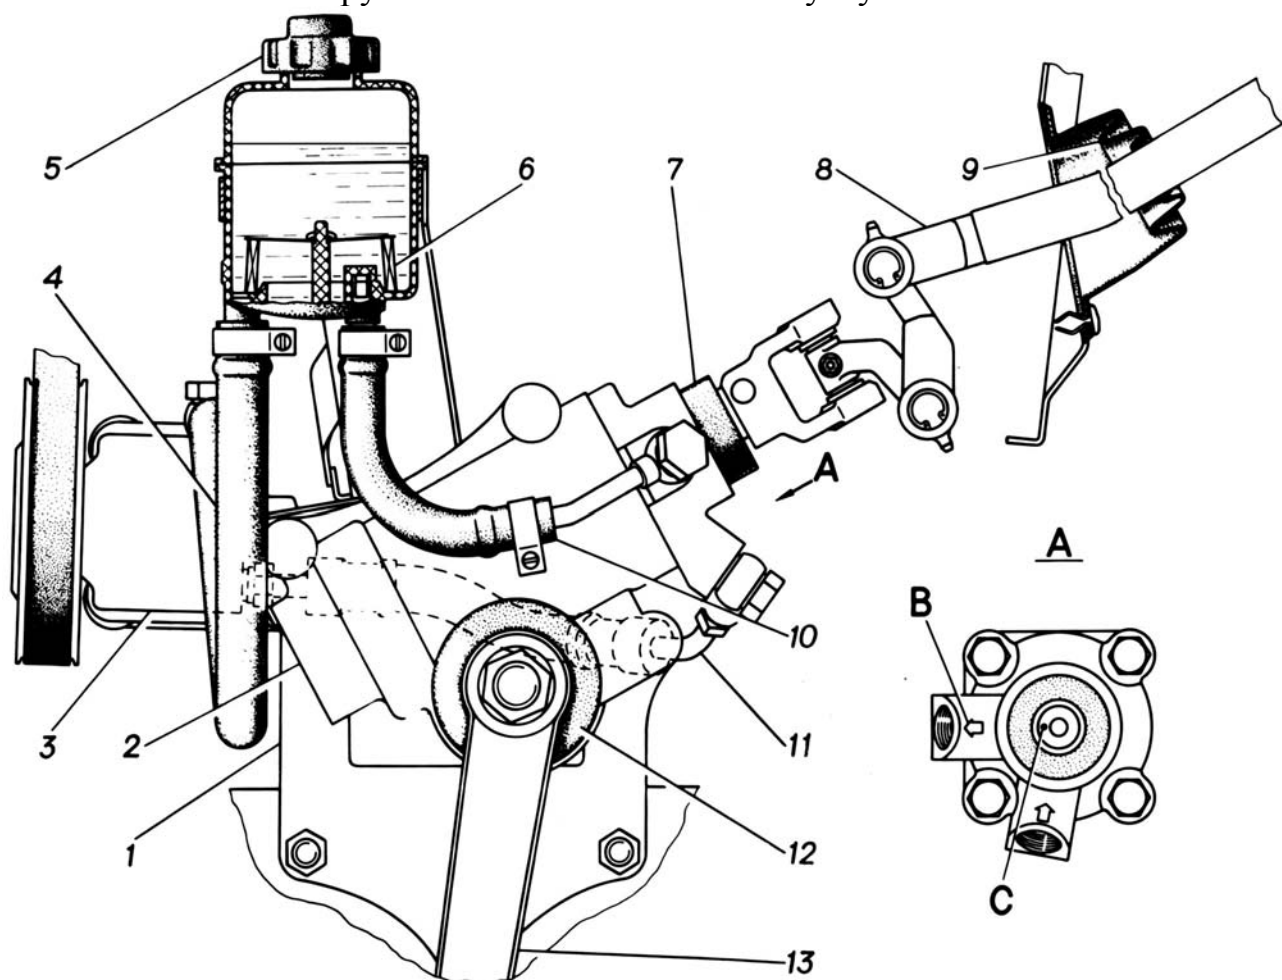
Рулевое управление с гидроусилителем: А – вид на входной вал (вилка условно снята); С – метка на входном валу; В – метка на механизме; 1 – кронштейн рулевого механизма; 2 – рулевой механизм; 3 – насос ГУР; 4 – шланг всасывающий; 5 – крышка; 6 – фильтрующий элемент; 7, 9 и 12 – уплотнители; 8 – карданный вал; 10 – шланг сливной; 11 – шланг нагнетательный; 13 – сошка
